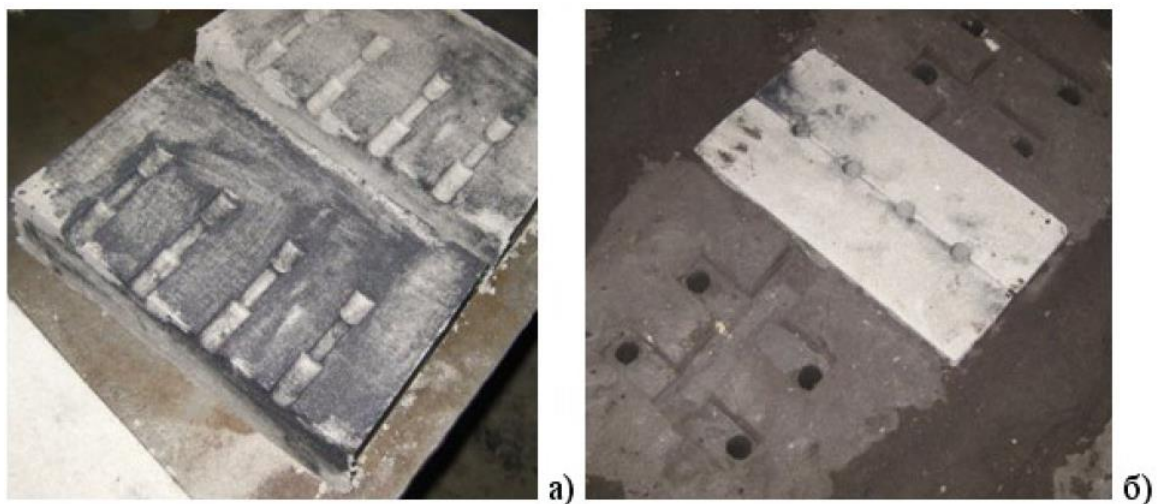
Підготовка ливарної форми до заливання:
